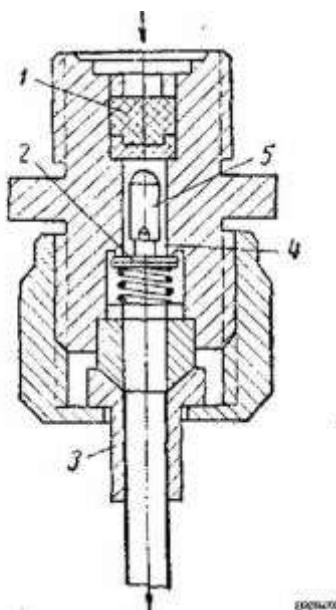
Дозирующий клапан для централизованной жидкой смазки.
